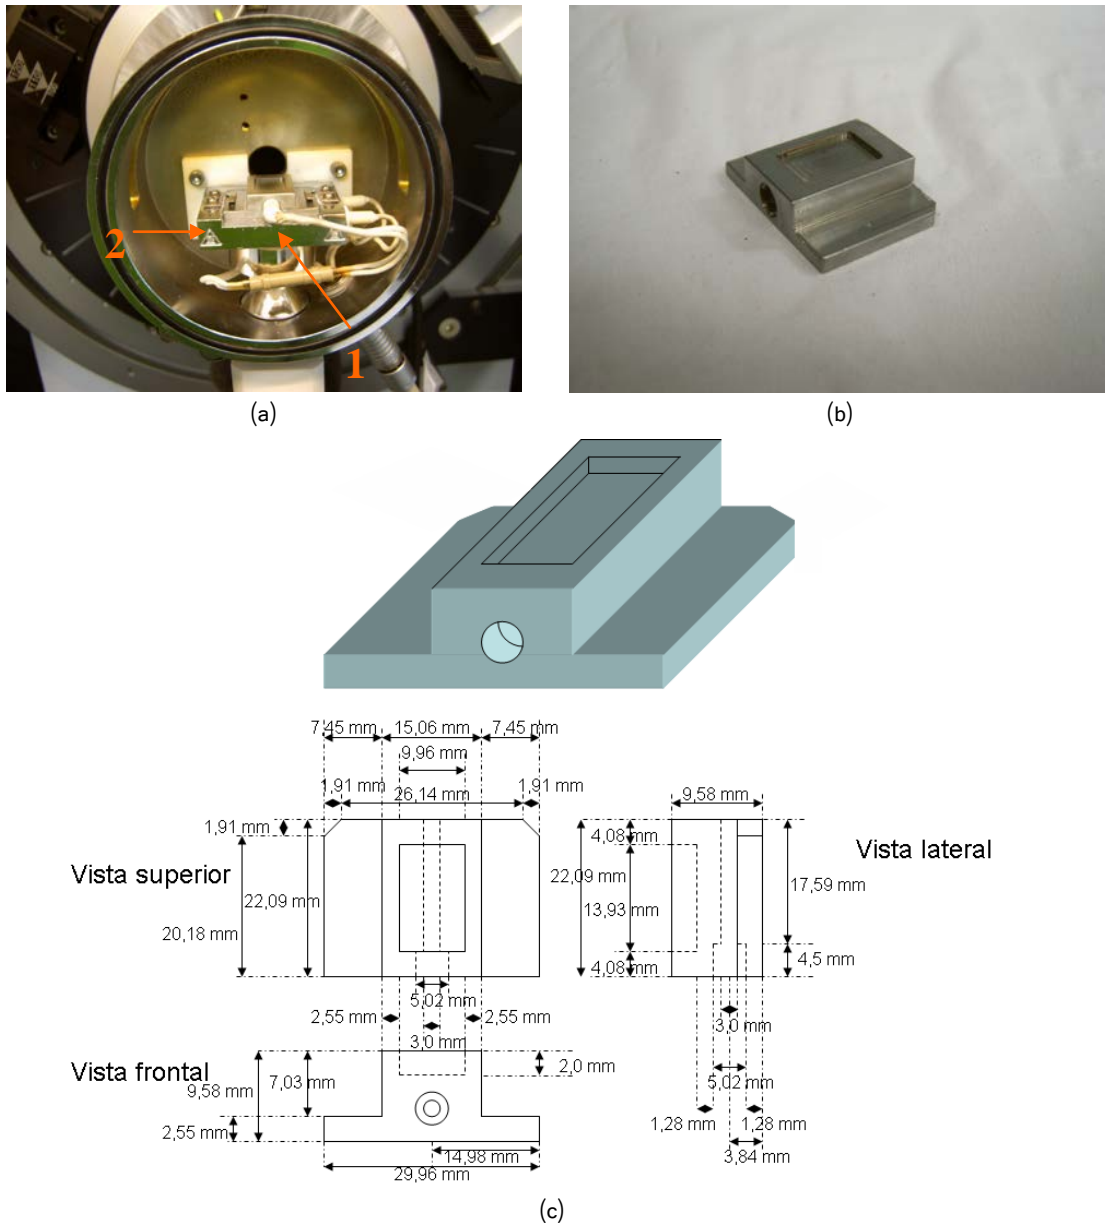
(a) Fotografía del portamuestras inicial montado adecuadamente en la cámara TTK 450. (b) Fotografía del portamuestras original. (c) Alzado, planta y perfil del portamuestras original.
